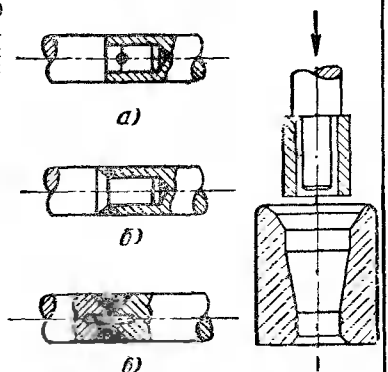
Способы восстановления деталей: а — при помощи установки нового хвостовика на резьбе; б — наделка лопового хвостовика запрессовкой с обваркой места соединения; в — запрессовкой нового хвостовика с посадкой на шпильку.
